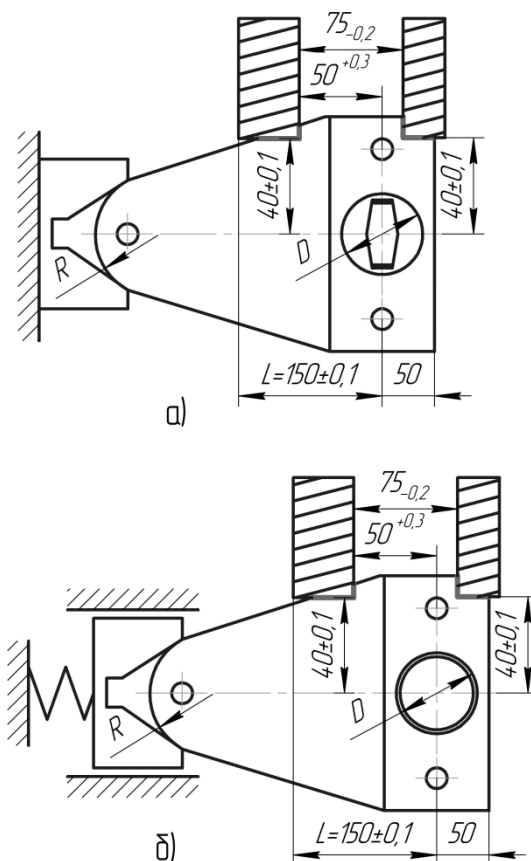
Схема установки заготовки на центруючий штифт і призму
